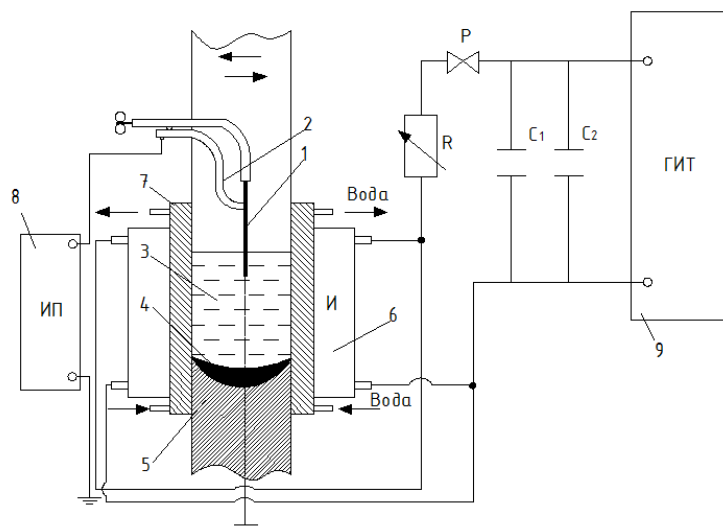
Схема ЭШС с сопутствующей электроразрядной обработкой; 1 – электрод; 2- токоподвод; 3- шлаковая ванна; 4 – металлическая ванна; 5- сварной шов; 6- индуктор; 7- формирующие планки; 8- источник питания; 9- генератор импульсных токов; Р – высоковольтный разрядник; C1,C2 – батареи высоковольтных конденсаторов; R- балластный реостат
